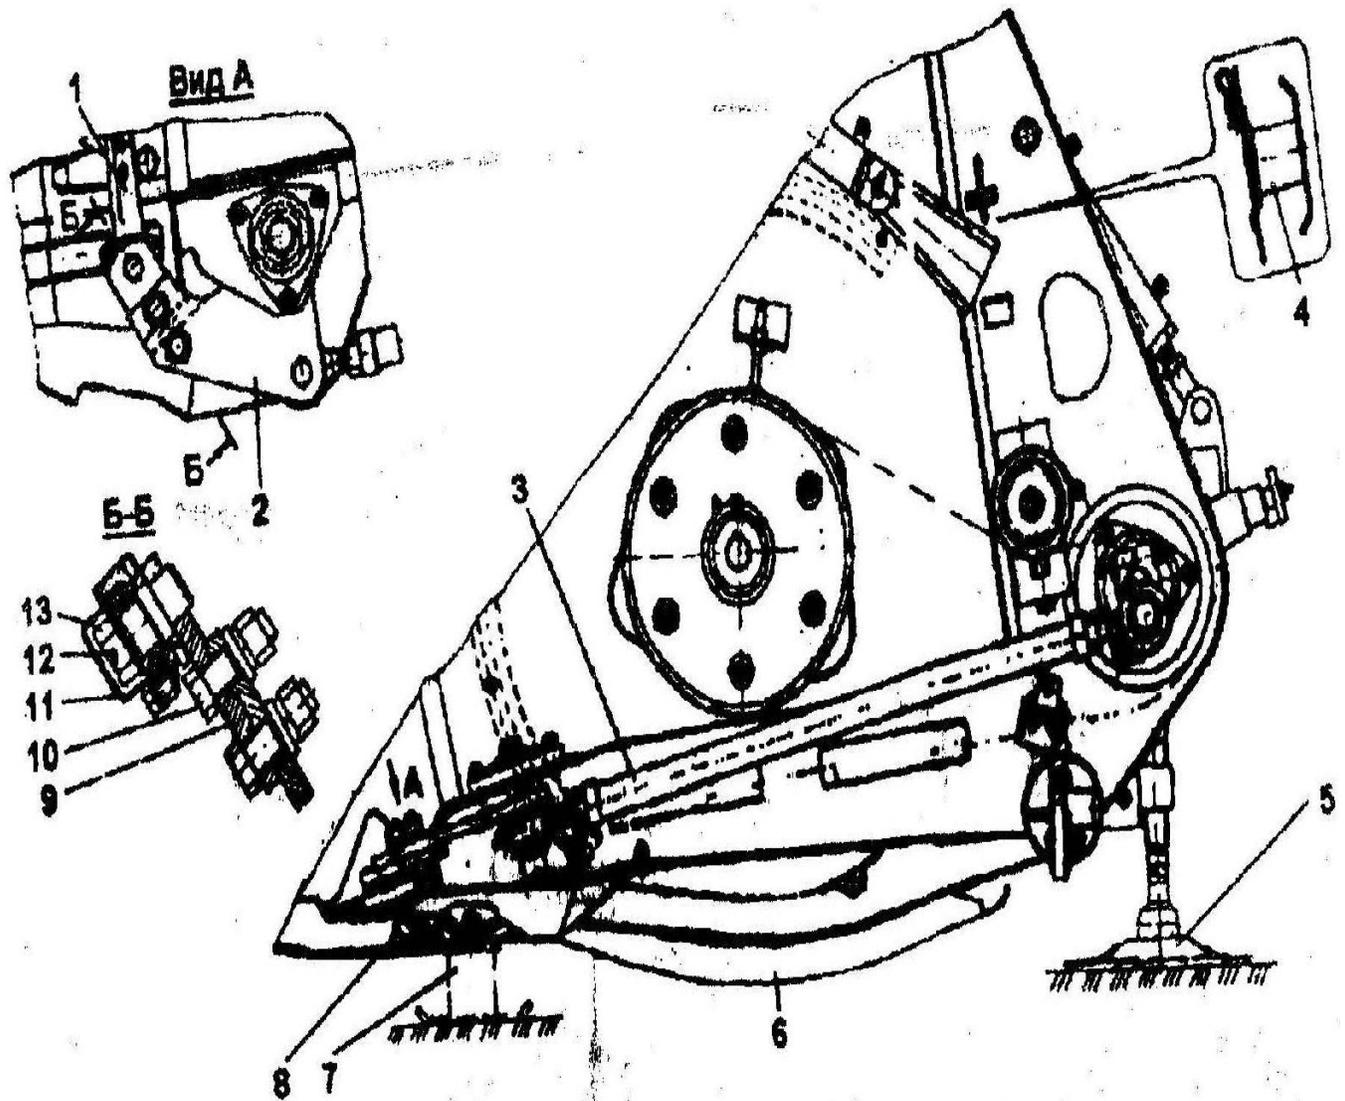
ПРИВОД НОЖА РЕЖУЩЕГО АППАРАТА:
